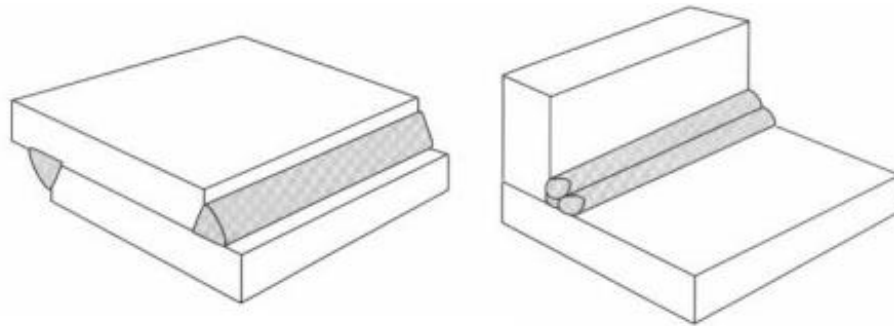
Tipos soldadura de filete; Izquierda Soldadura de filete de una pasada de ambos lados den una junta solapada; Derecha: Soldaduras de filete de múltiples pasadas de un solo lado en una junta en "L".
